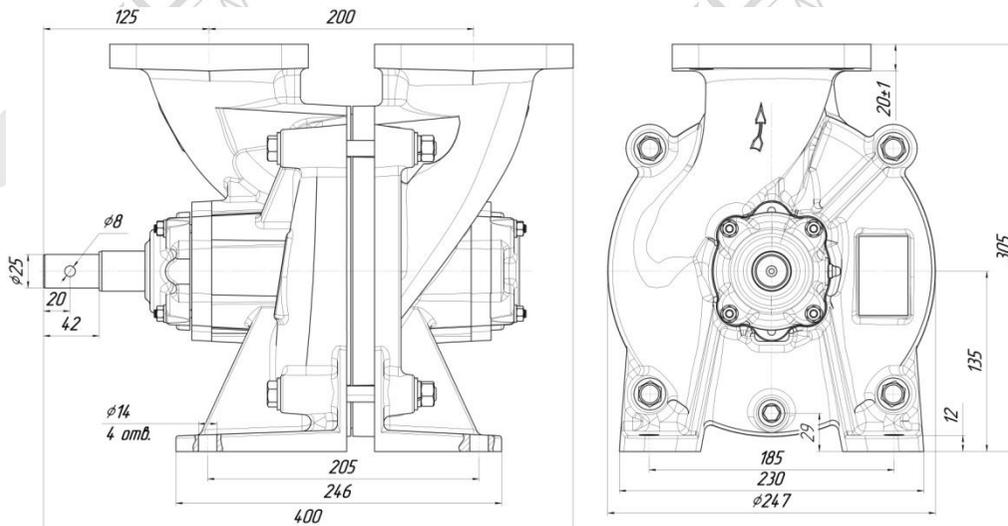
Габаритные и присоединительные размеры насосов правого вращения.
